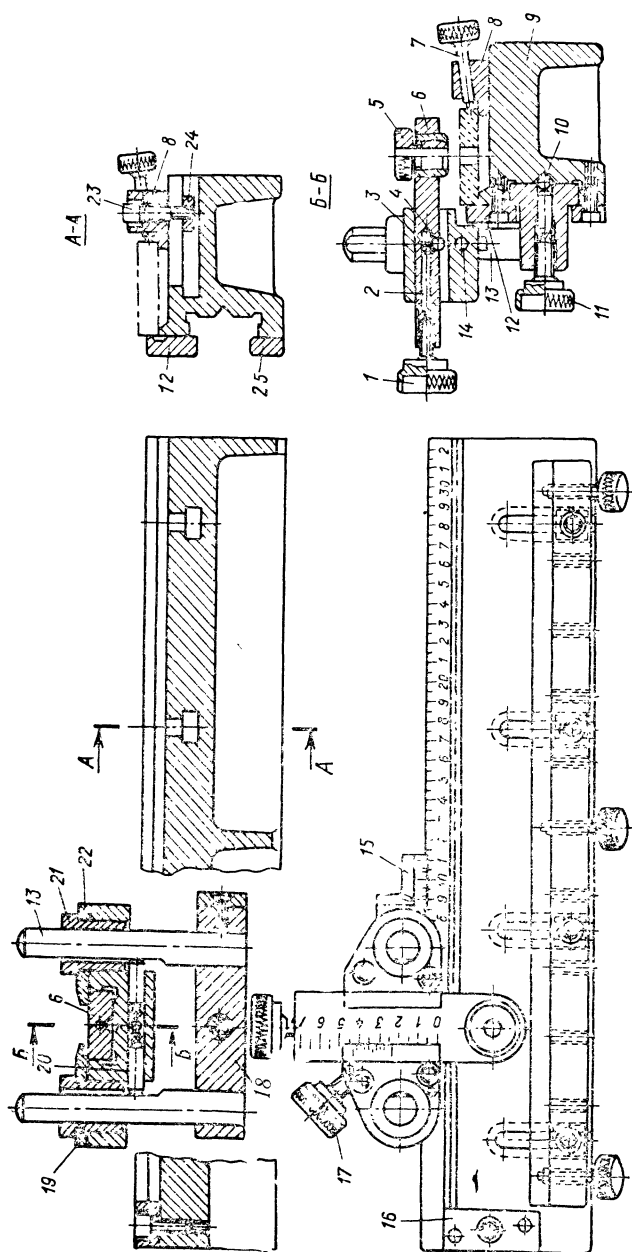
Переналаживаемый кондуктор для сверления отверстий в деталях типа плит
